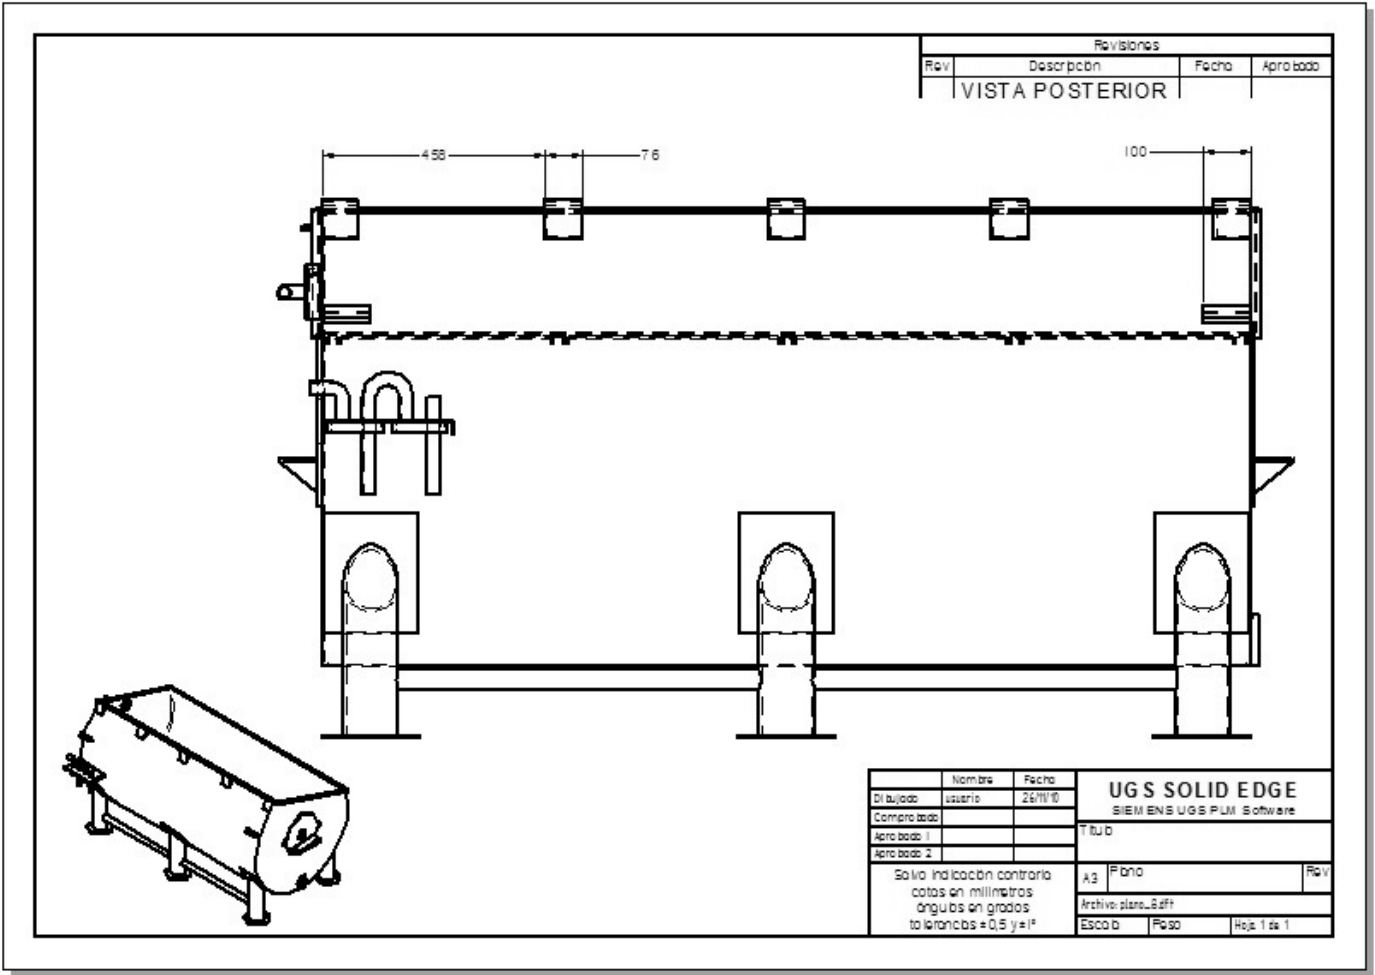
Plano del contenedor de mezclado, vista posterior, detalle 6.
